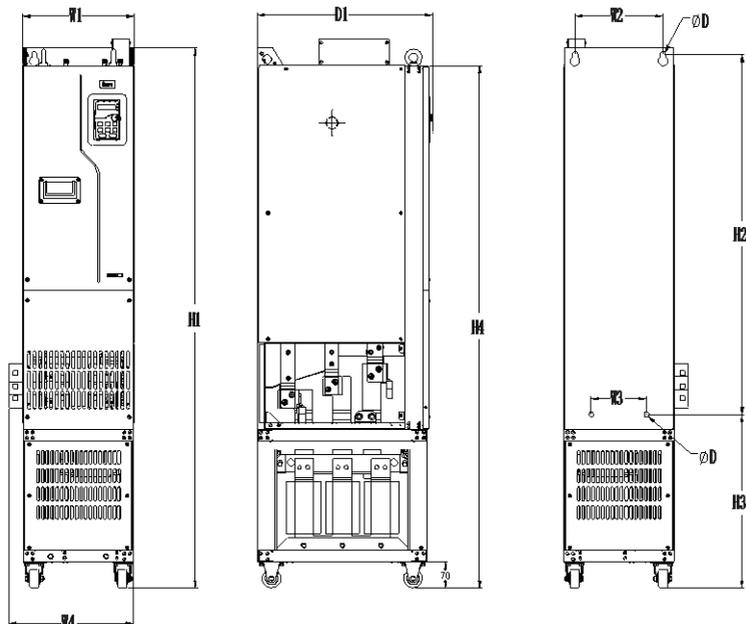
Чертеж для напольного монтажа моделей ПЧ 380В 220-500кВт с выходными дресселями
